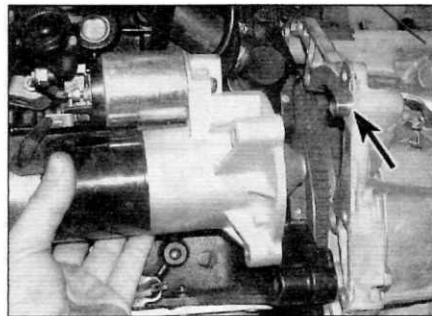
Снимите стартер и установочный штифт (отмечен стрелкой) (показан дизельный двигатель)
